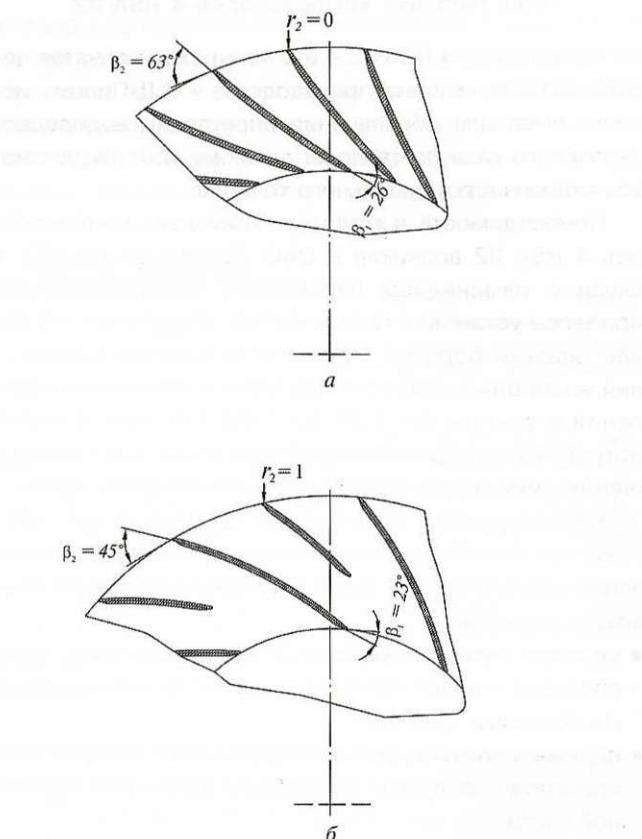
Новая (а) и штатная (б) лопаточные решетки колес компрессора 5RSA56
